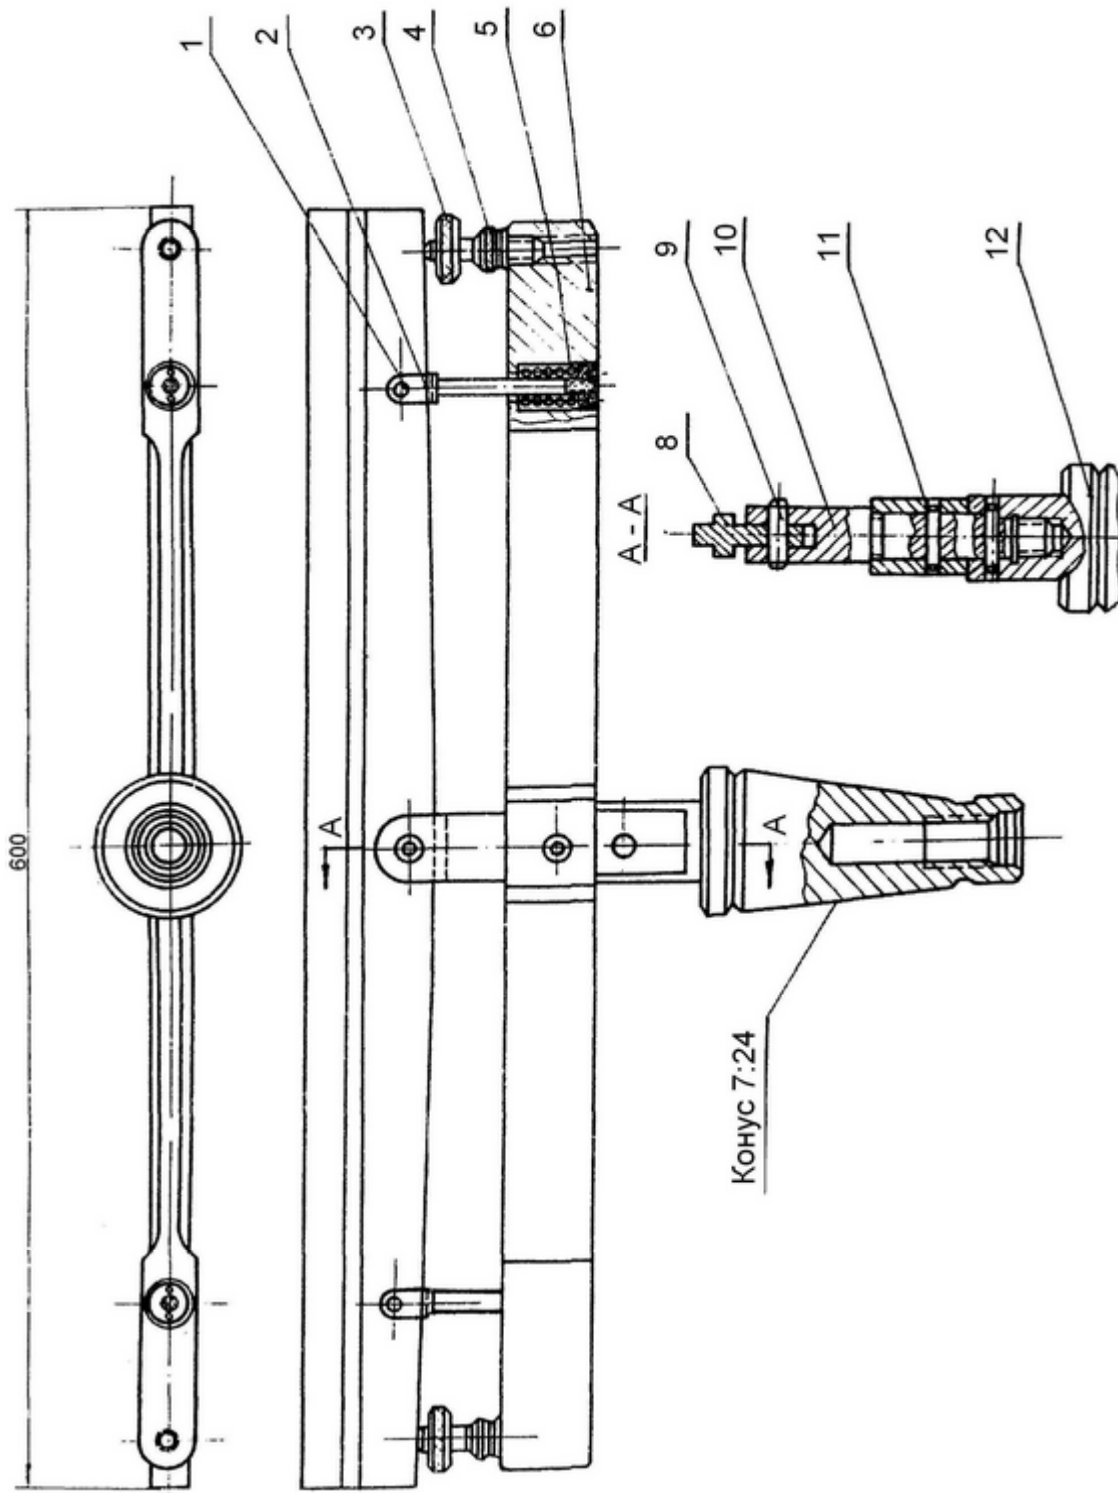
Приспособление для проверки перпендикулярности оси шпинделя относительно направляющих стола горизонтально-фрезерного станка СД 8532 – 4004
